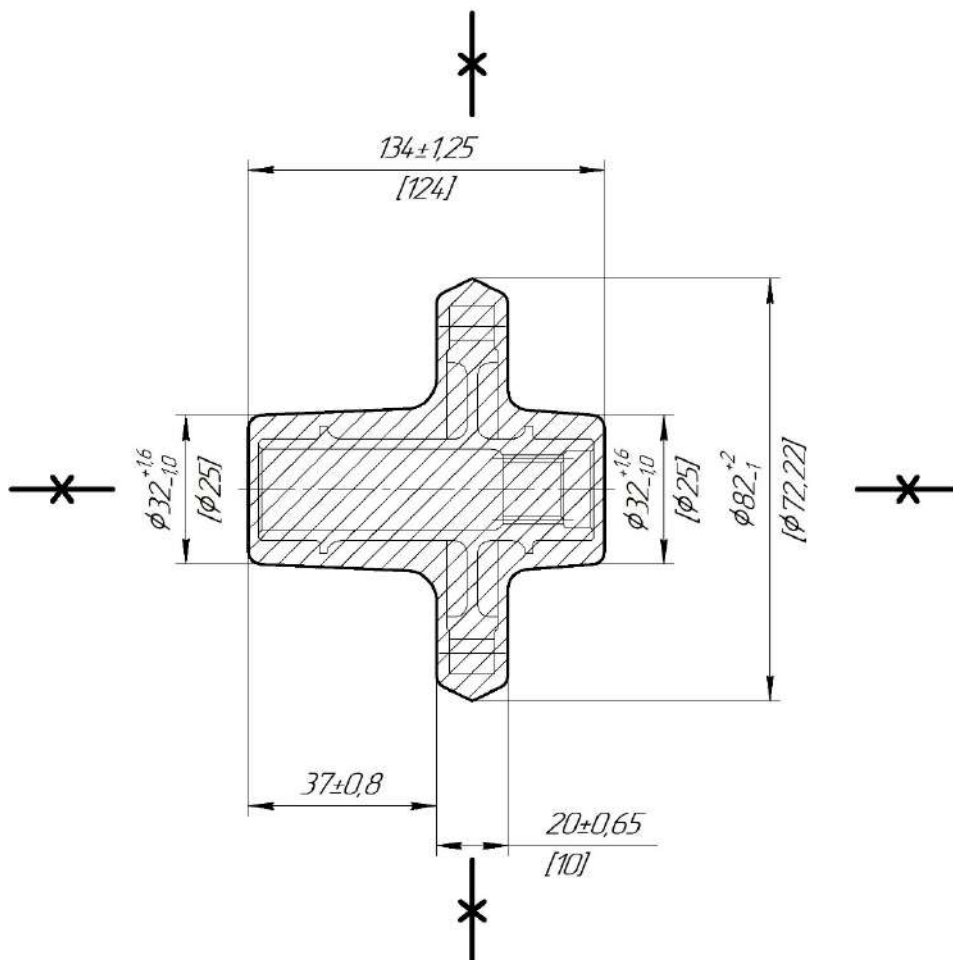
Рисунок заготовки, що отримана штамповкою на ГKM
